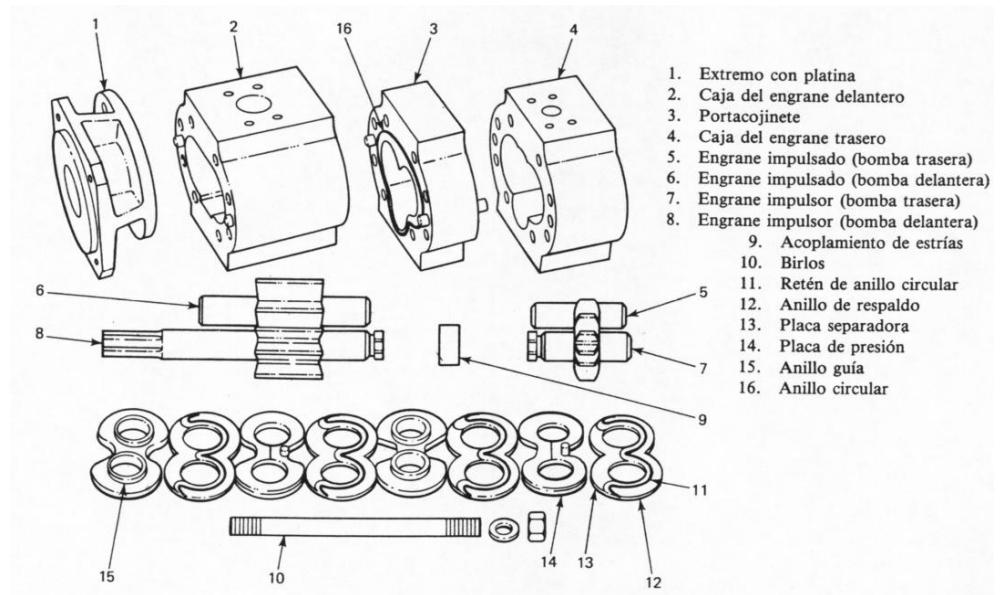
Componentes de una bomba de engranes de varios pisos
